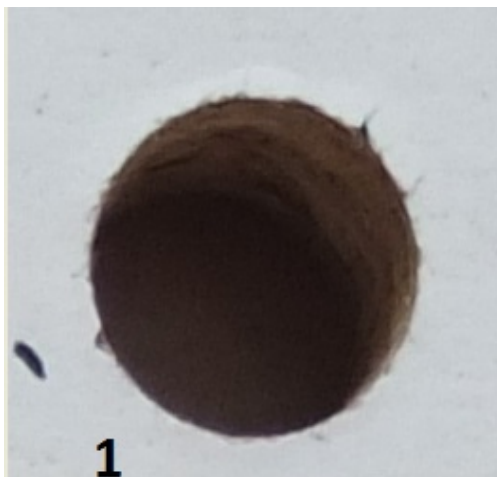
Внешний вид отверстия выполненного сверлом после первого цикла затупления (вид со стороны входа инструмента)
